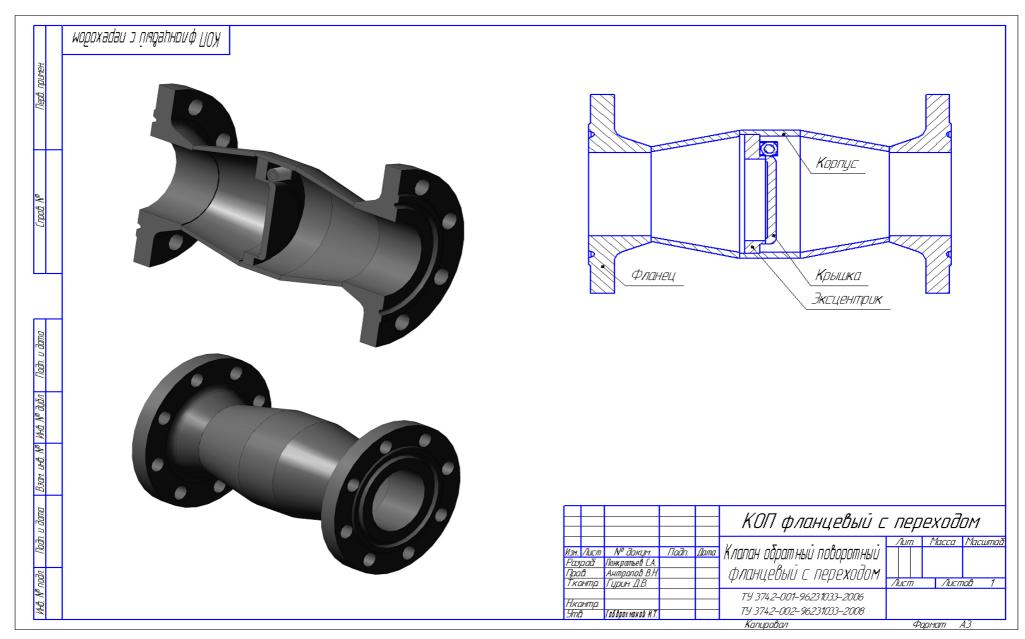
Клапан обратный поворотный фланцевый с переходом
